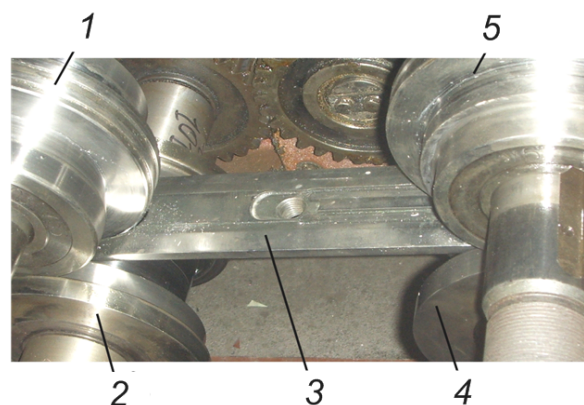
Межклетьевая проводка скольжения, разработанная ОАО «Ульяновский НИИТ»: 1 – верхний ролик текущего перехода; 2 – нижний ролик текущего перехода; 3 – межклетьевая проводка скольжения; 4, 5 – нижний и верхний ролики последующего перехода
